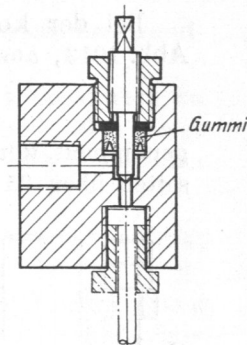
Spindelabdichtung mittels gespaltenen Gummirings.
